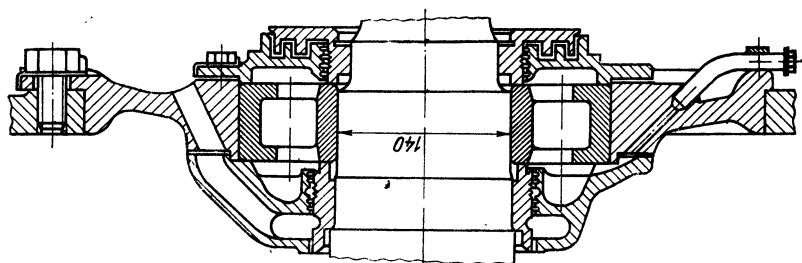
Задний подшипниковый щит теплового двигателя
